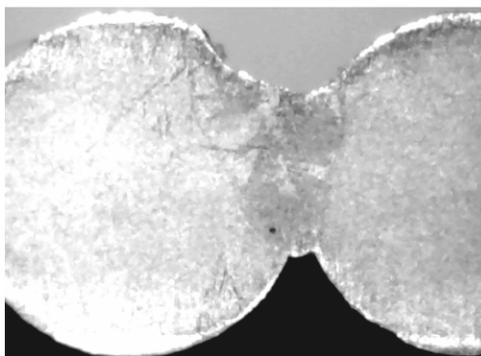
Макроструктура сварного шва после лазерной сварки
